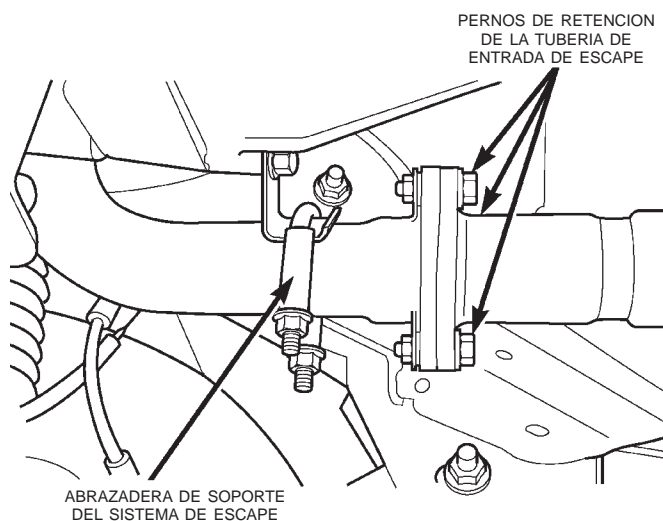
Conexión de la tubería de entrada del sistema de escape
